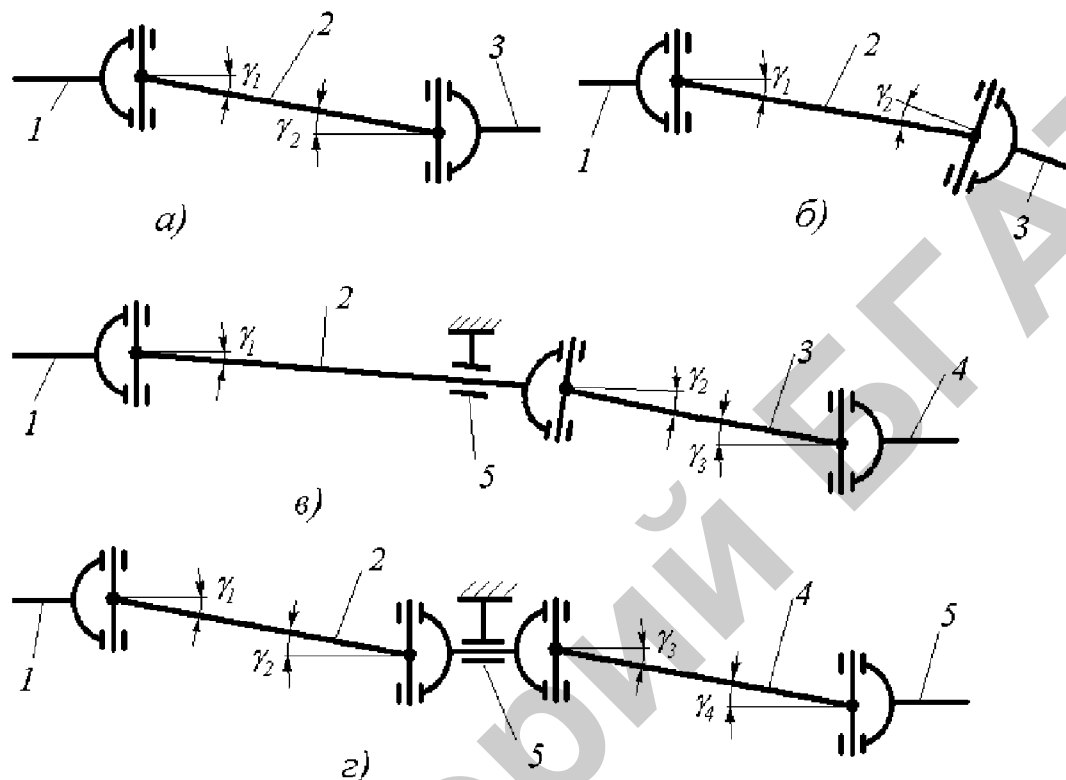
Основные схемы карданных передач с шарнирами неравных угловых скоростей: а, б – с двумя шарнирами и одним валом; в – с тремя шарнирами, двумя валами и промежуточной опорой; г – с четырьмя шарнирами, двумя валами и промежуточной опорой; γ – углы между валами
